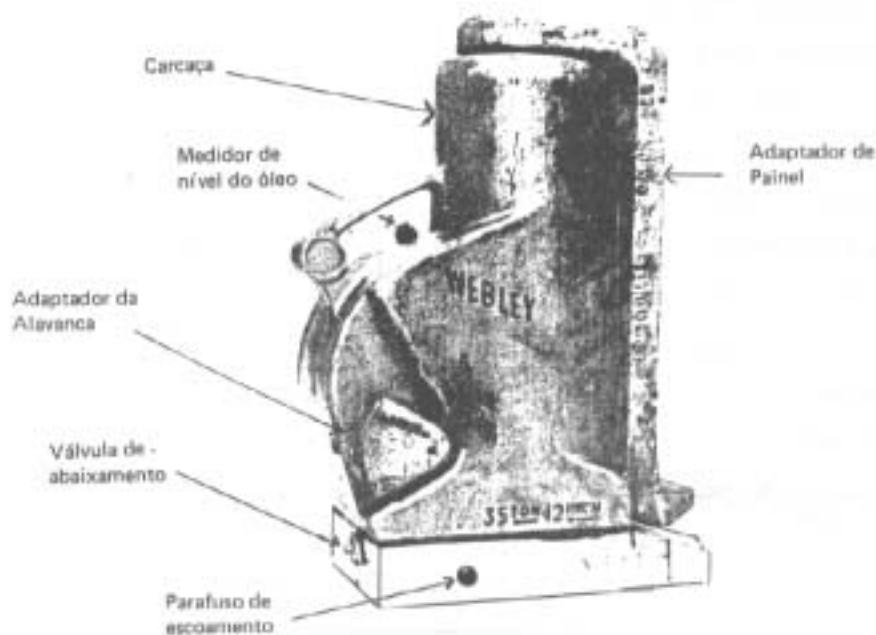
Macaco WEBLEY com Adaptador de Painel.
